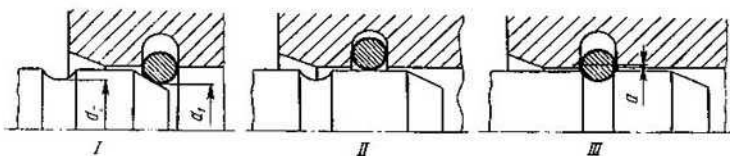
Fijación mediante un anillo de resorte colocado en el rebajo de la pieza exterior:
